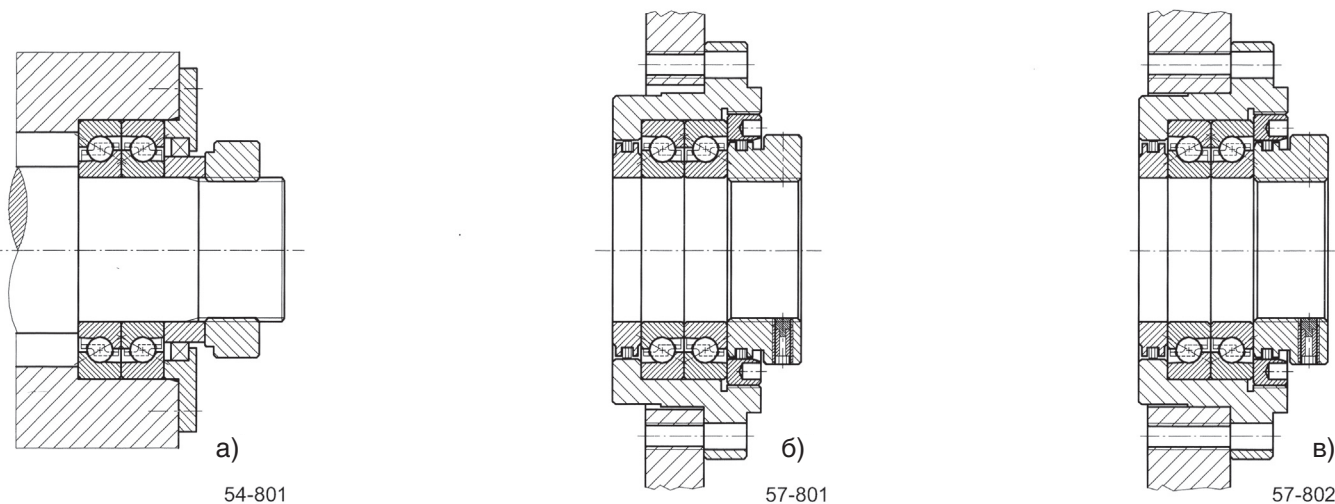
Разработка удобных для изготовления и монтажа подшипниковых узлов шарико-винтовых пар.
